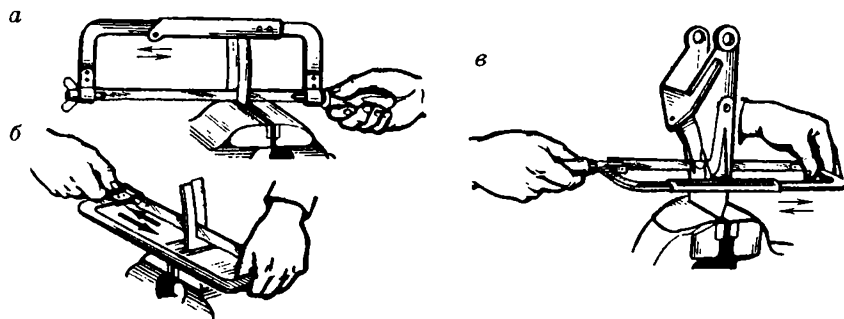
Резка ножовкой при глубоких прорезях:
